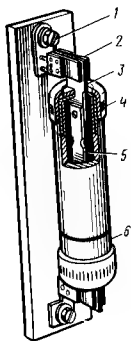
Предохранитель разборный с фибровой трубкой типа ПР:
